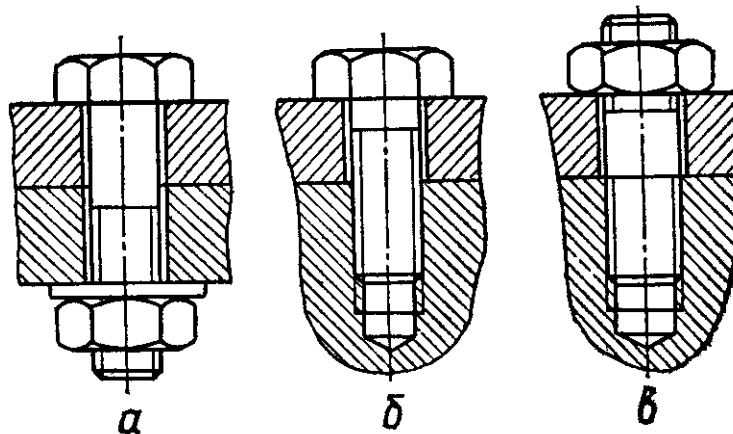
З'єднання за допомогою болта, гвинта та шпильки
